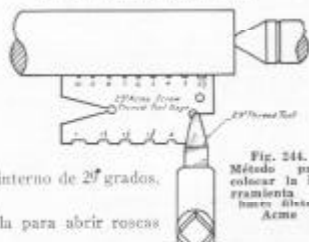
Método para colocar la herramienta al hacer filetes Acme
